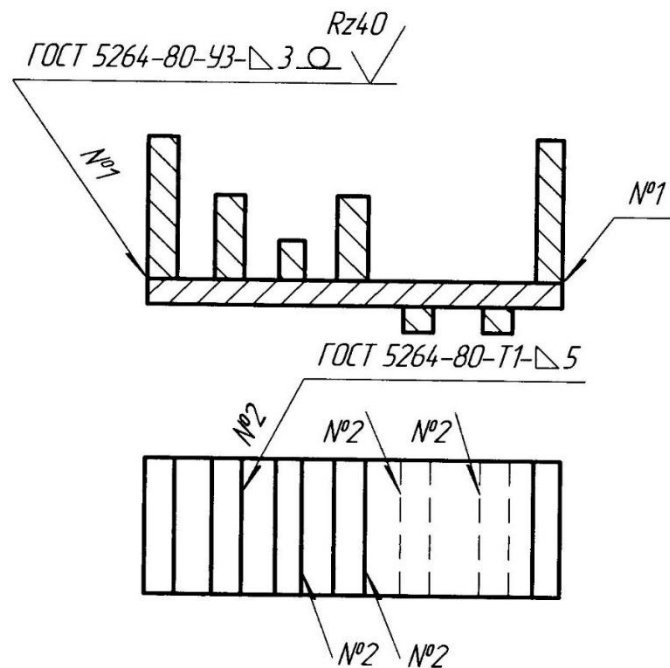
Обозначение одинаковых сварных швов
